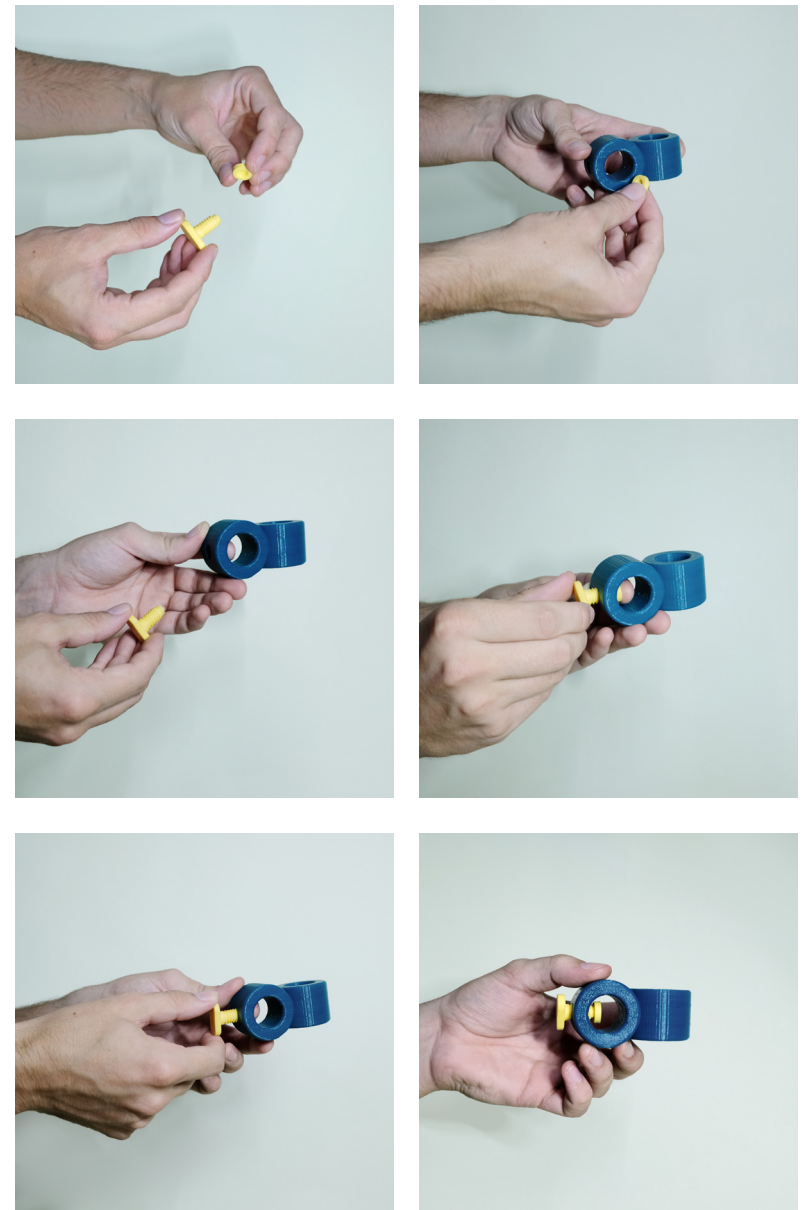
Explicação de como colocar o parafuso e travão na peça perpendicular
